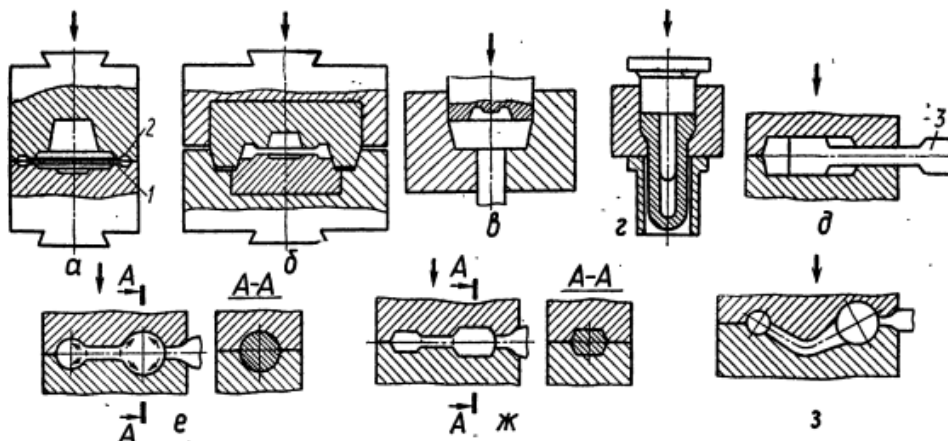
Схемы горячей объёмной штамповки и заготовительных ручьёв: а - открытый штамп, б - закрытый штамп, в - штамп с двумя плоскостями разъёма, г - штамповка выдавливанием, д - протяжка, е - подкатка, ж - формовка, з – гибка
